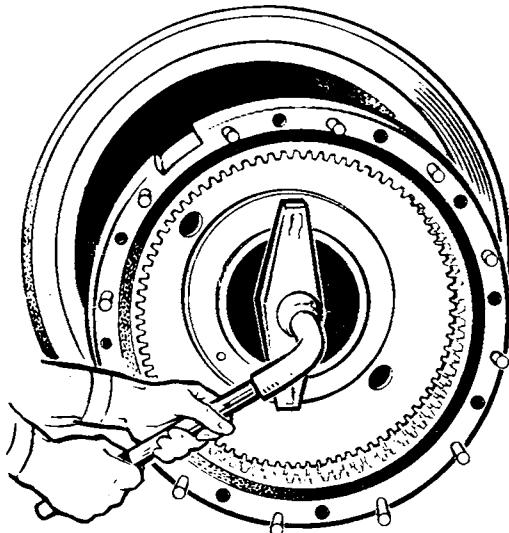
Отвертывание гайки подшипника ступицы заднего колеса
